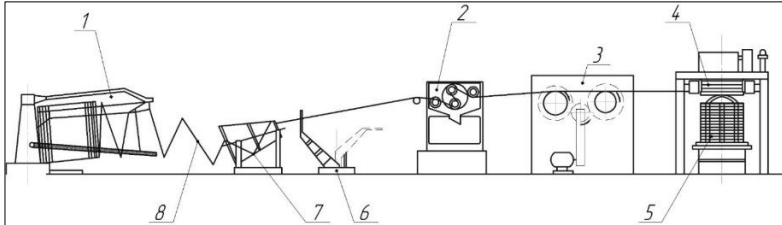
Лінія для виготовлення холоднодеформованого арматурного прокату в мотках: 1 – розмотувальний пристрій; 2 – окалиномател; 3 – пристрій для холодного деформування прокату; 4 – приводний намотувальний механізм; 5 – пристрій, що формує моток; 6 – датчик аварійної зупинки лінії; 7 – блок для вирівнювання арматурного стрижня; 8 – арматурний стрижень
